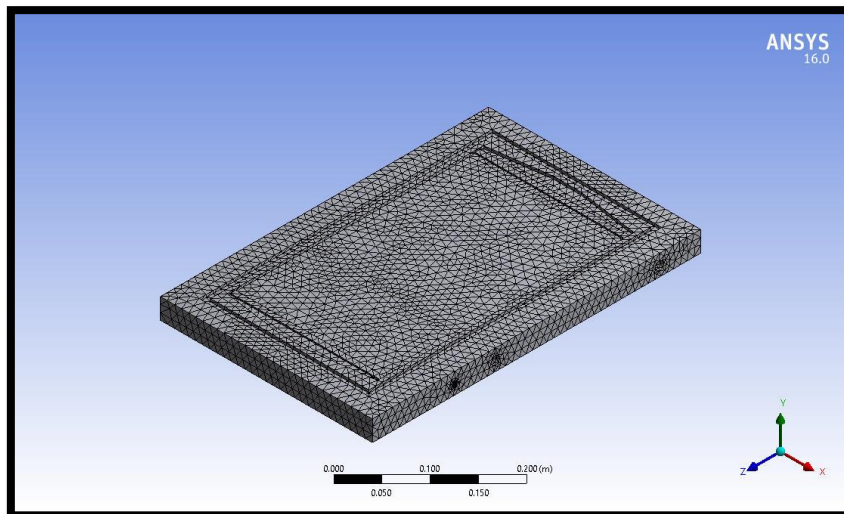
Vista isométrica de mallado de molde (tapa inferior) para espécimen.
